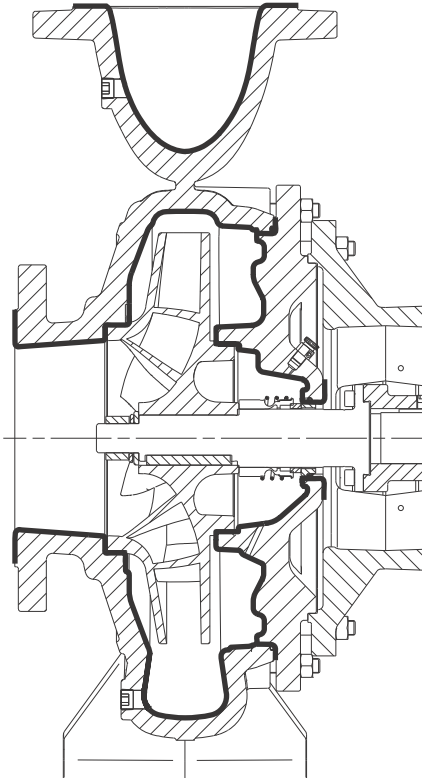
Schnittzeichnung von Pumpen mit einer verschleißfesten Beschichtung
